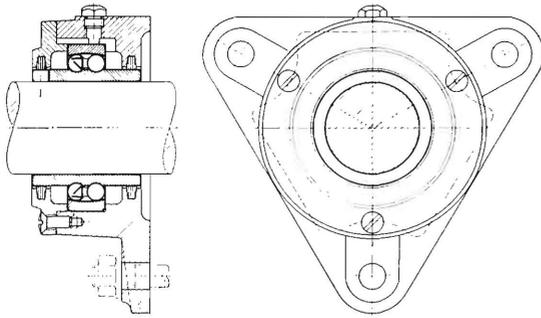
Flanschlagergehäuse und Pendelkugellager mit breitem Innenring.
